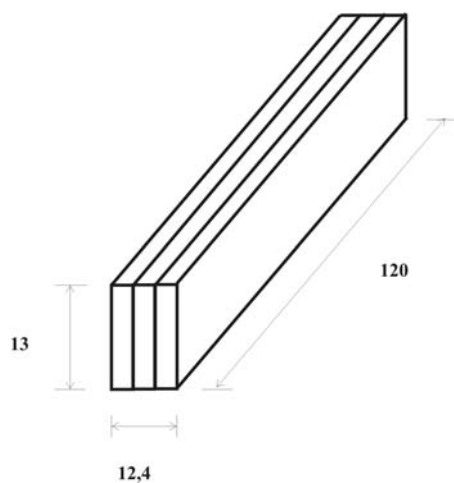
Dimensões, em mm, do corpo de prova na configuração de impacto na borda da placa
